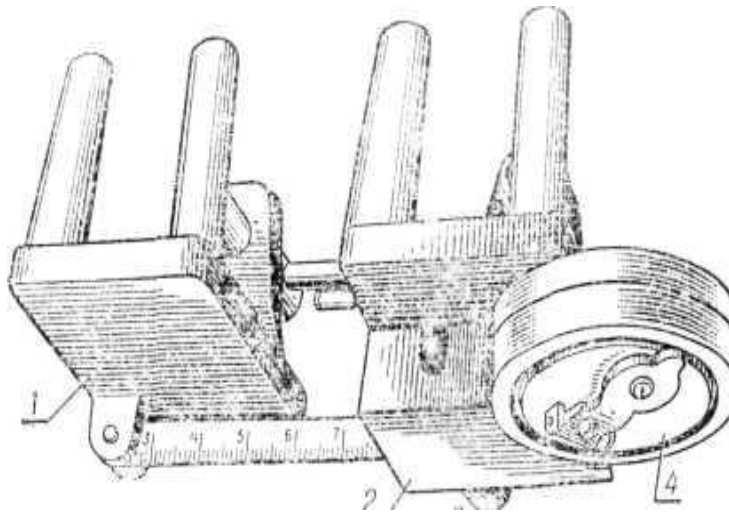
Пристрій для визначення величини зносу гусеничного ланцюга: 1 - лівий корпус; 2 - правий корпус; 3 - важіль стопора; 4 - рулетка.
